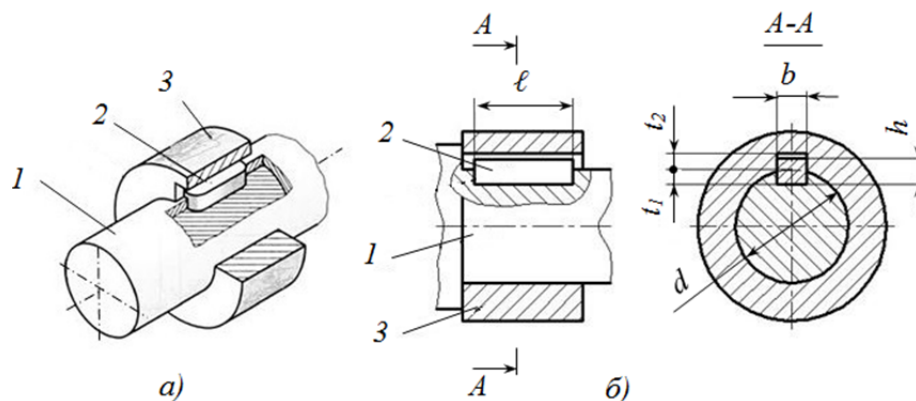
Загальний вигляд (а) та креслення шпонкового з'єднання (б):
